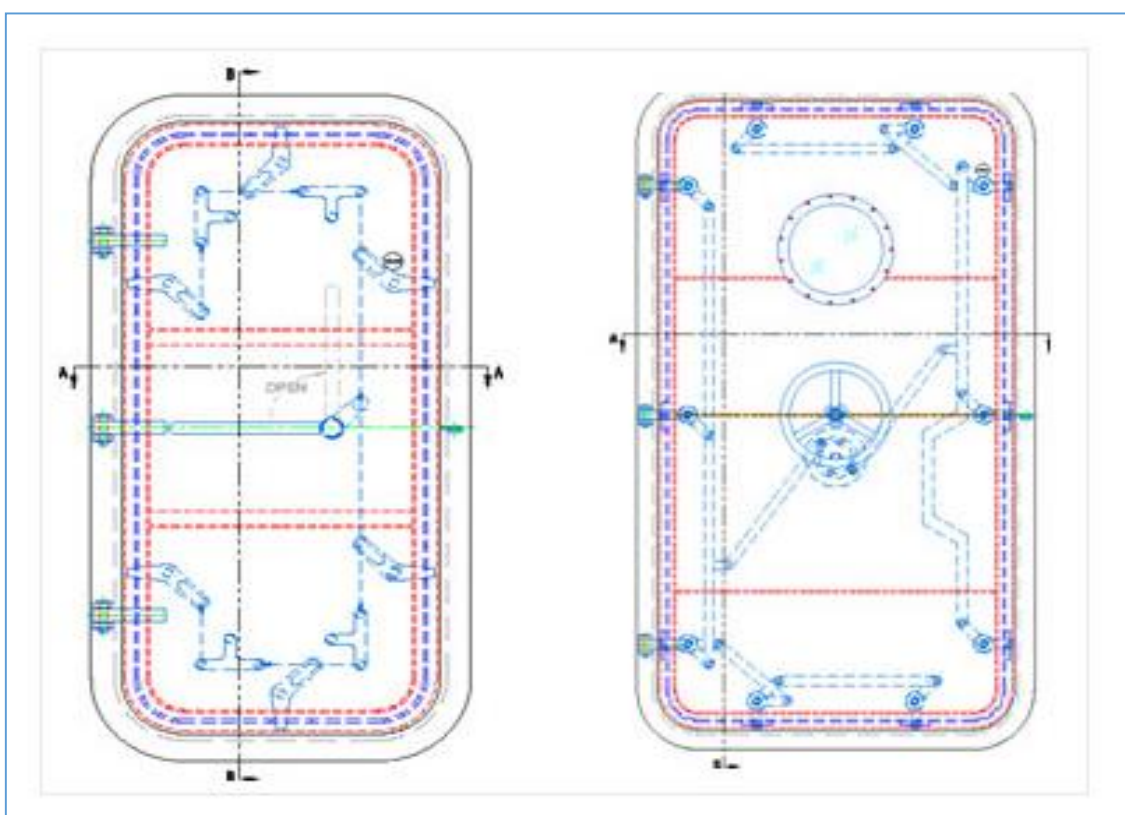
Watertight Doors.Fonte: Watertight Doors, 2014.
